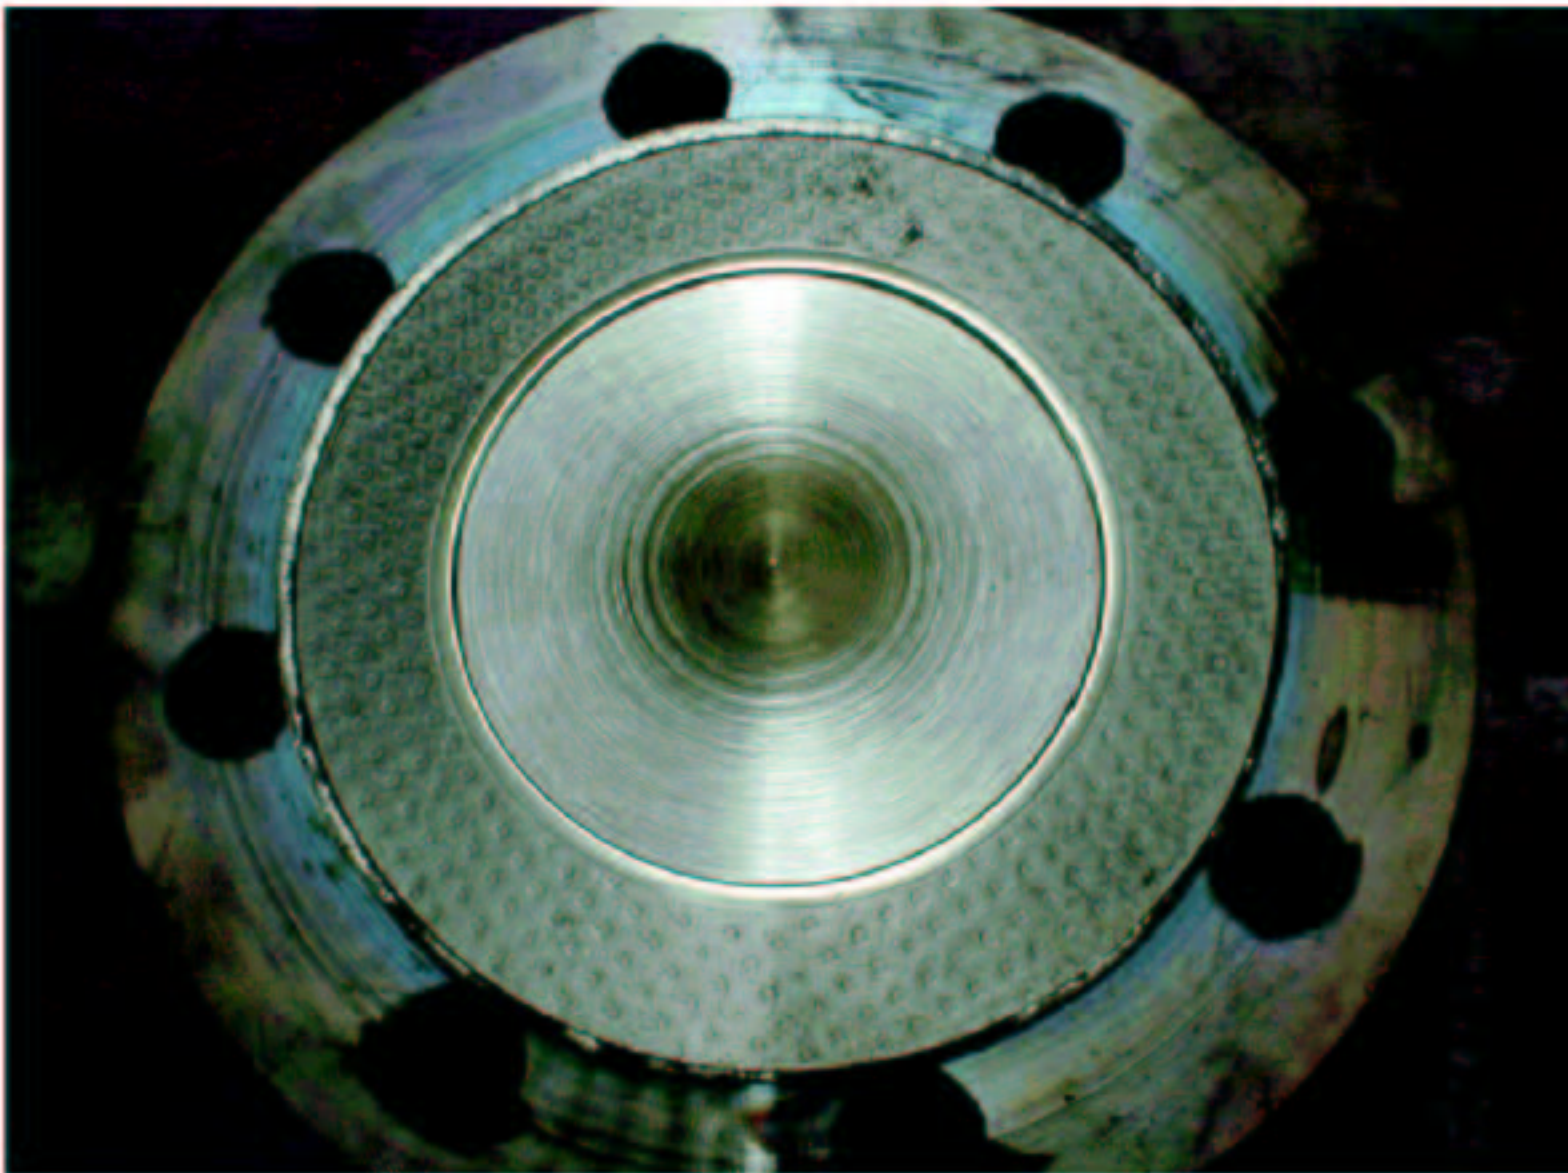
Detailaufnahme, Flansch mit anhängender Dichtung
